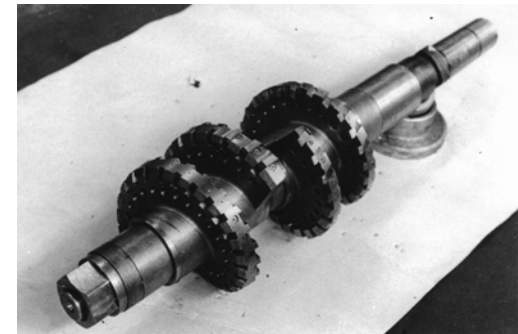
Фреза червячная "Победа" со вставными режущими элементами $m=36$
